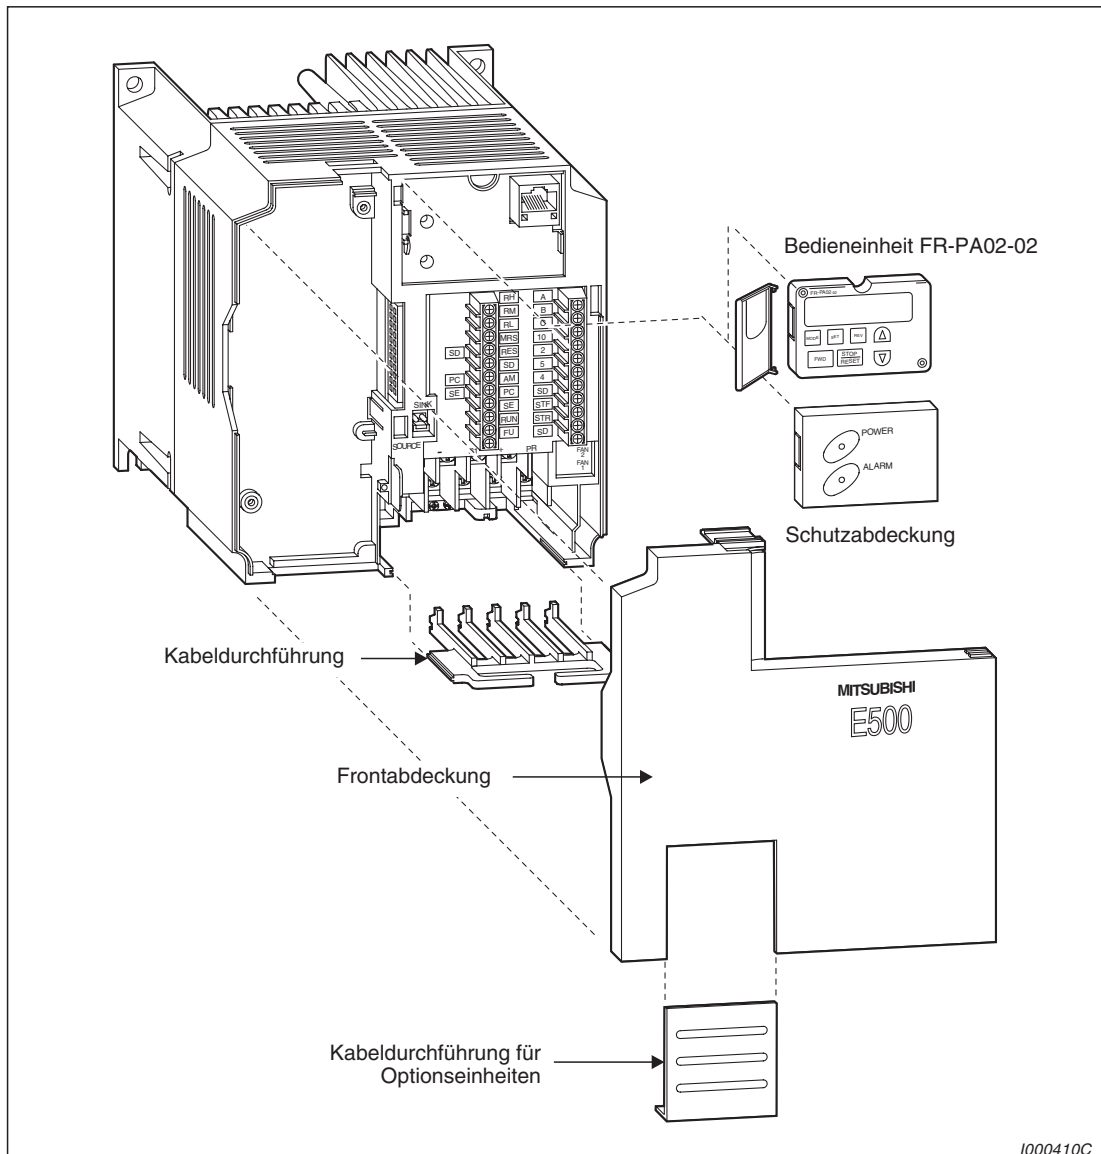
Gehäusekomponenten des FR-E 500 EC
